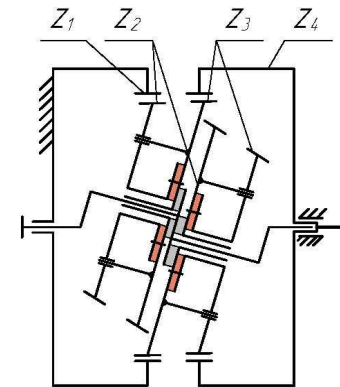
Кинематическая схема планетарного редуктора с наклонными сателлитами:
